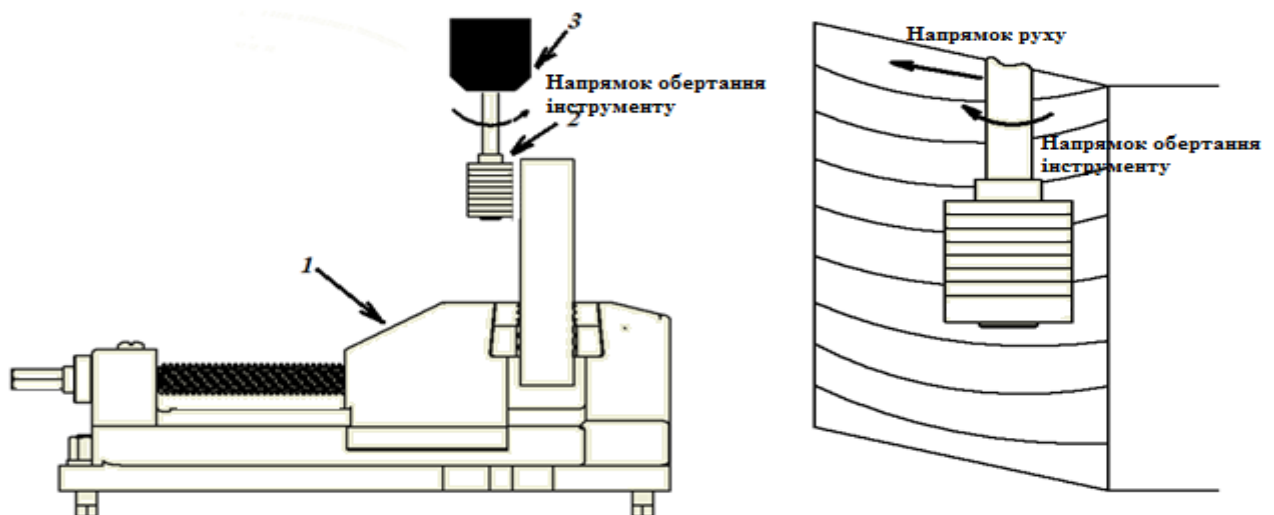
Схема оброблення плоских поверхонь: 1) лещата; 2) інструмент;
